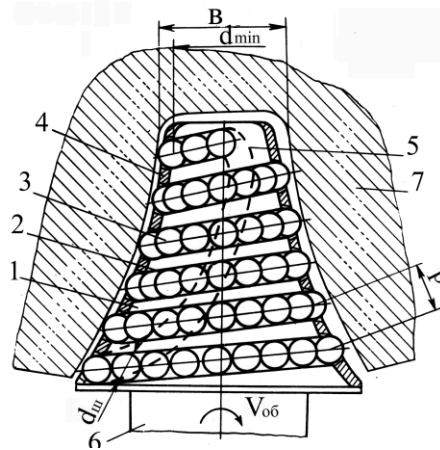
Пристрій для обкатування кульками зубчатих коліс, гвинтів, рейок
